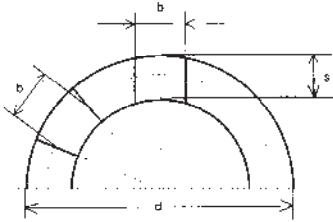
Probenquerschnitt bei Probekörper aus Rohren.
